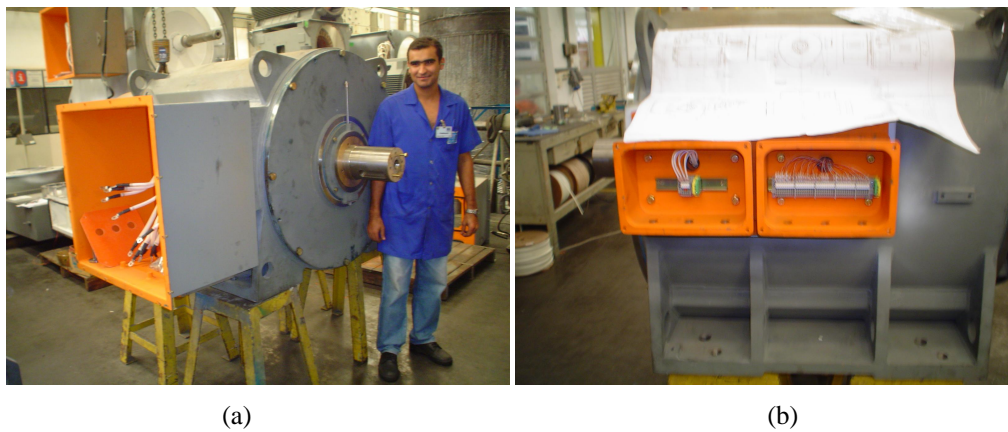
(a) Máquina montada, (b) Caixas de ligações dos acessórios.
